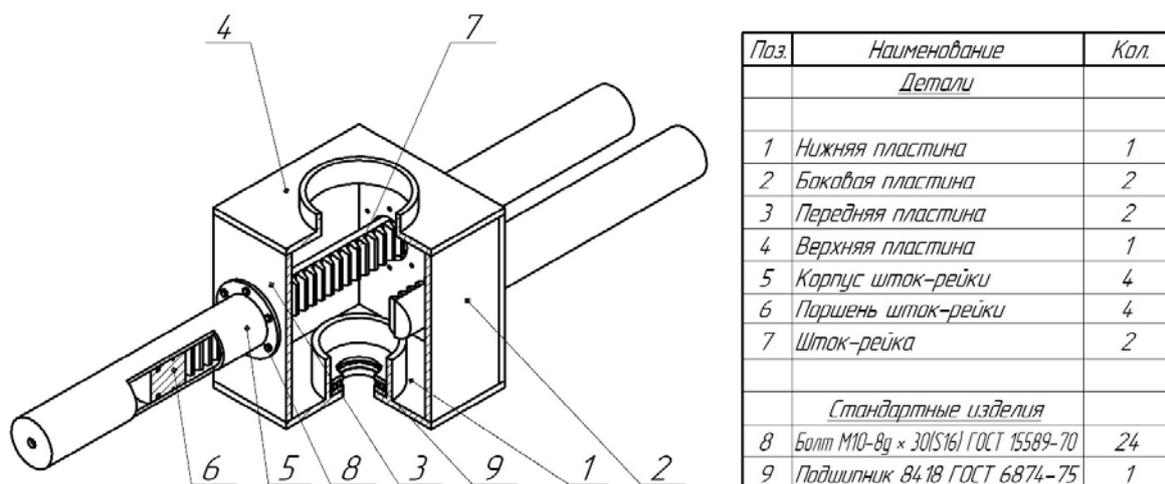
Чертеж корпуса опорно-поворотного устройства
